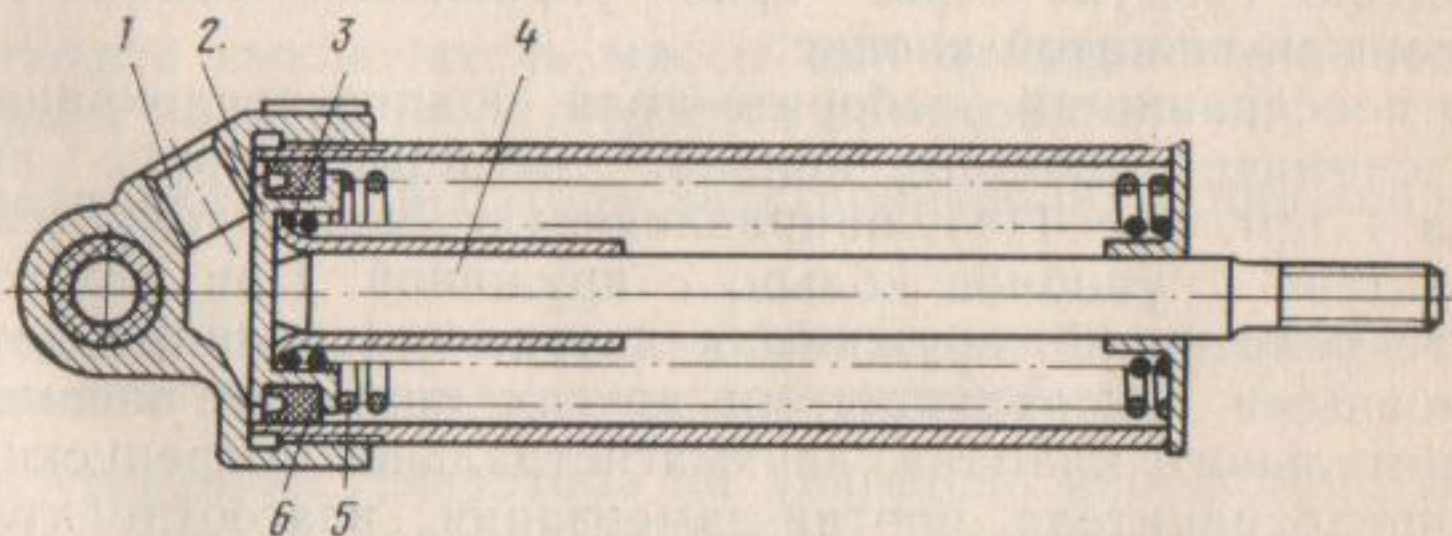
Пневматический цилиндр привода заслонки механизма вспомогательного тормоза:
